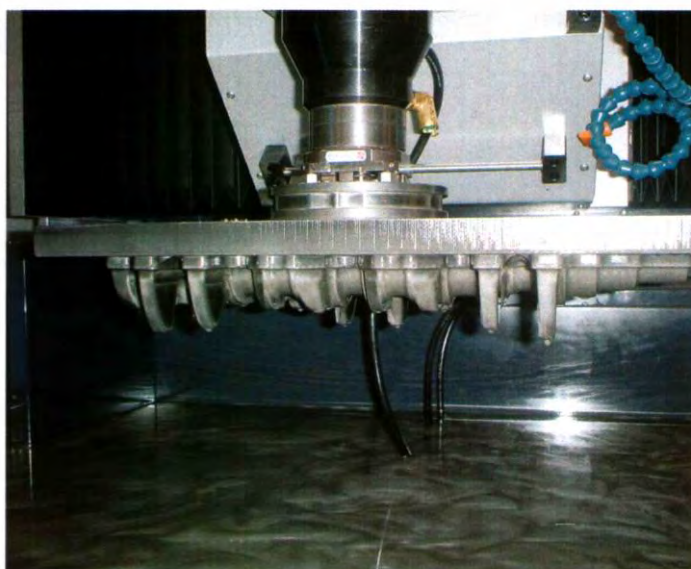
Способ установки крупногабаритного электрода-инструмента на станке с помощью переходной плиты и обработанная полуформа
